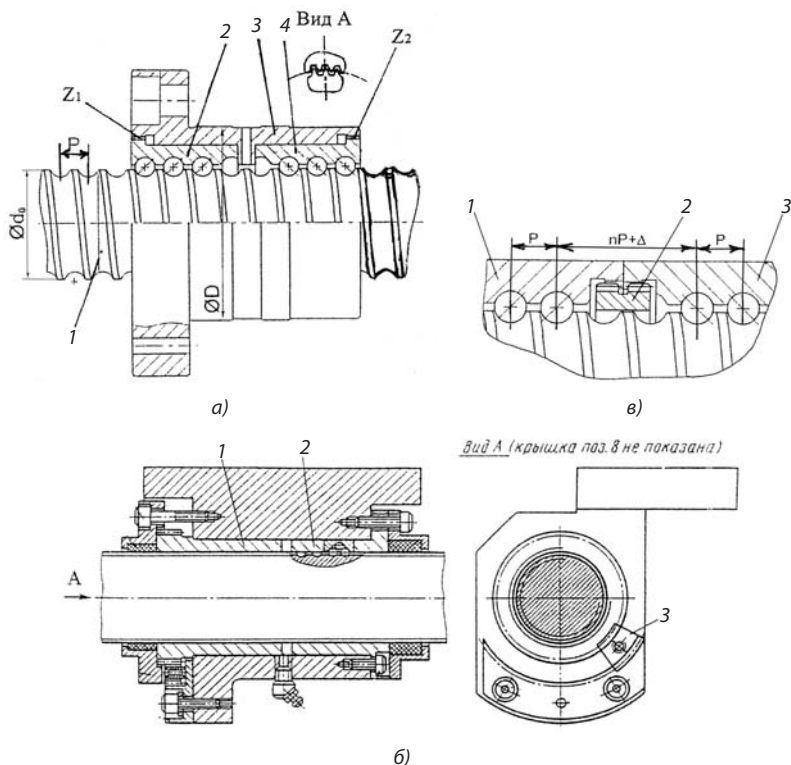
Конструкции ШВП с разными способами создания предварительного натяга:
